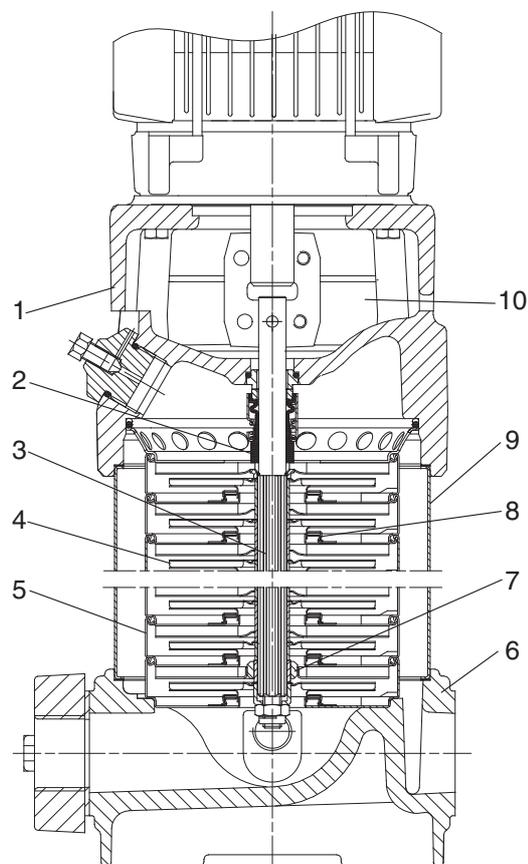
Plano seccionado CR 3, CR 5, CR 10
